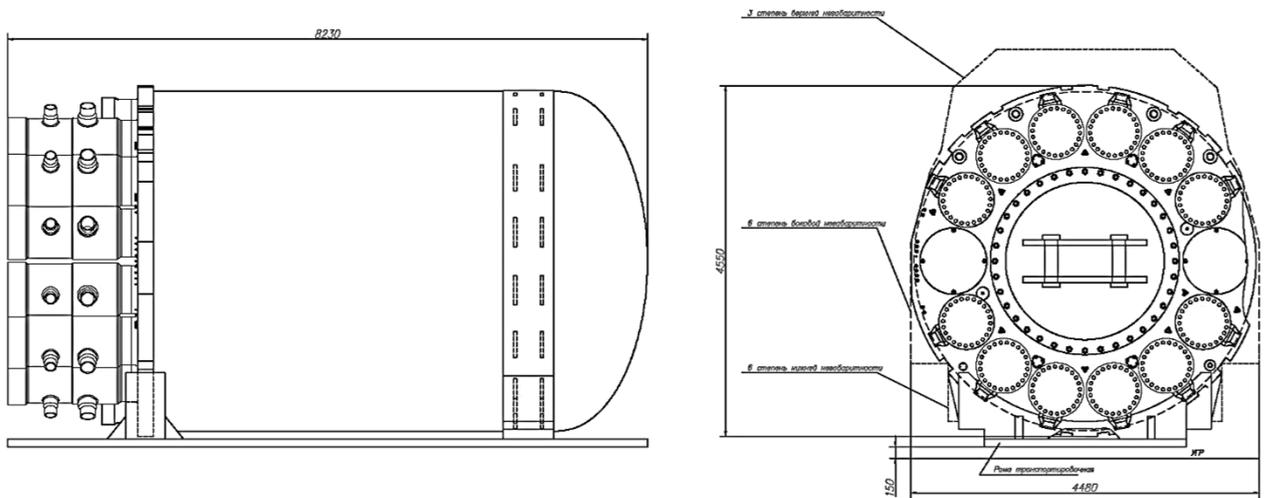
Транспортная упаковка моноблока реактора
